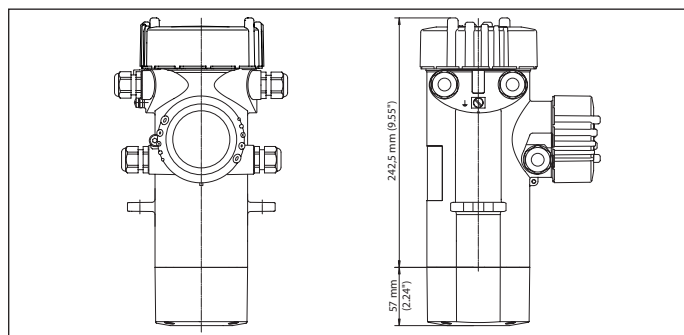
Корпус из алюминия или нержавеющей стали (точное литье)
